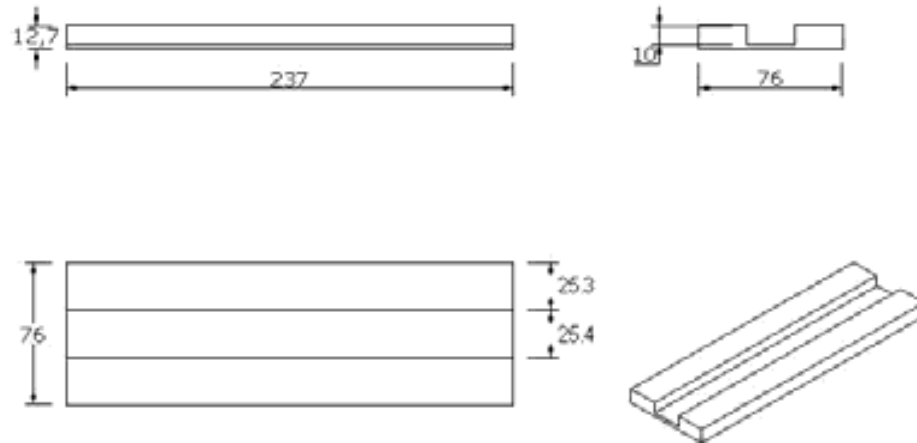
Dimensionamento de molde de CP para caracterização estática de SMAHC, dimensões em mm.
